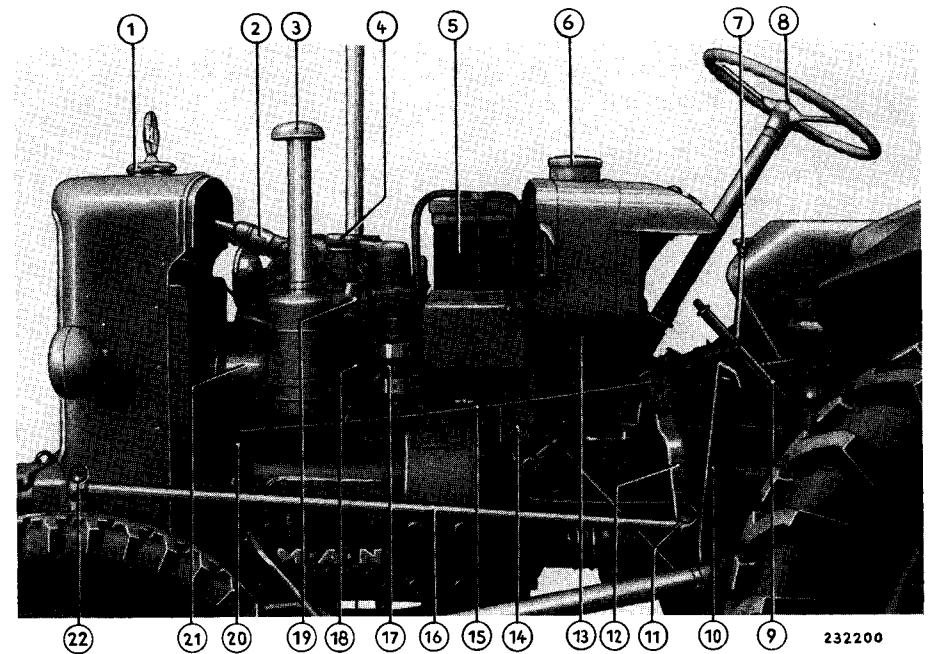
Vue de devant du véhicule et vue de gauche du moteur
